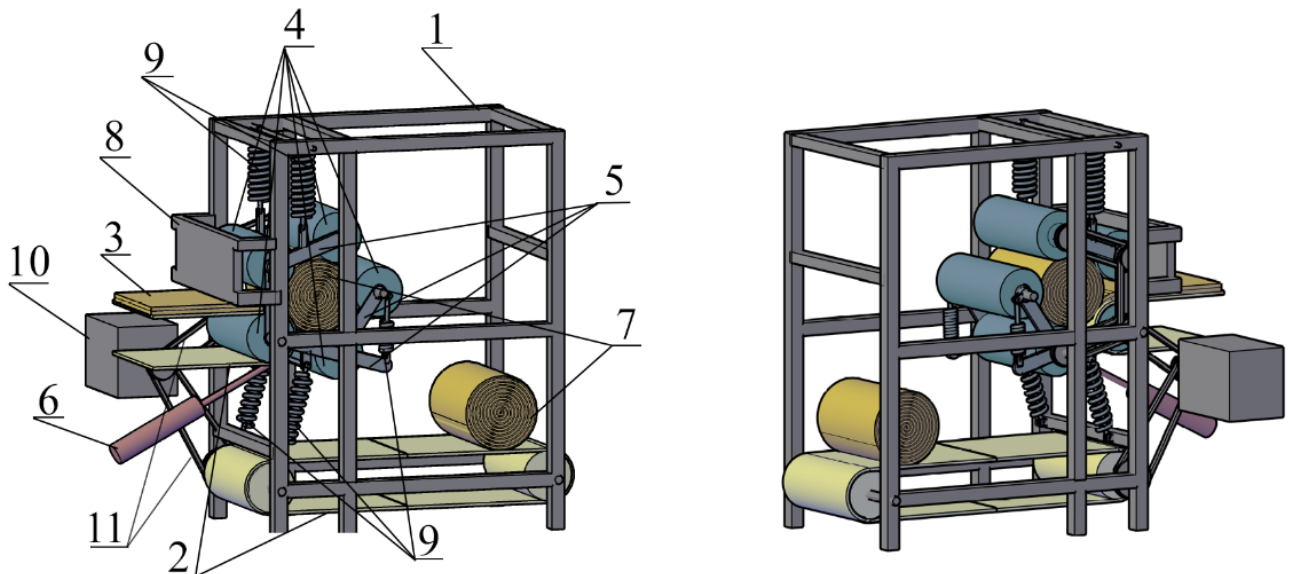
КПЗО для виготовлення ПР: а – вид спереду, б – вид ззаду, 1 – рама, 2 - транспортерна стрічка, 3 - БССК, 4 – ролики, 5 – підпружинені рамки, 6 – гідроциліндр, 7 - ПР, 8 – обмежувальна планка, 9 – пружини стиску, 10 – електродвигун, 11 – клинові паси
